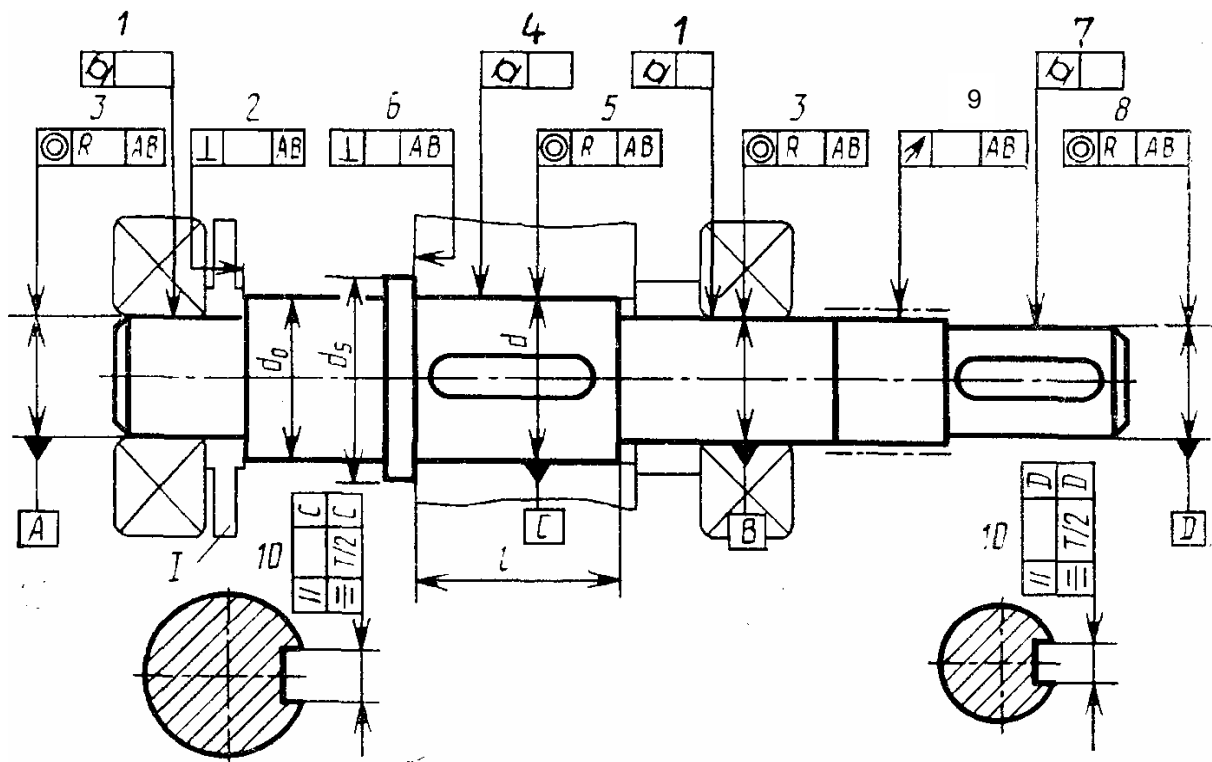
Обозначение допусков формы и расположения вала
